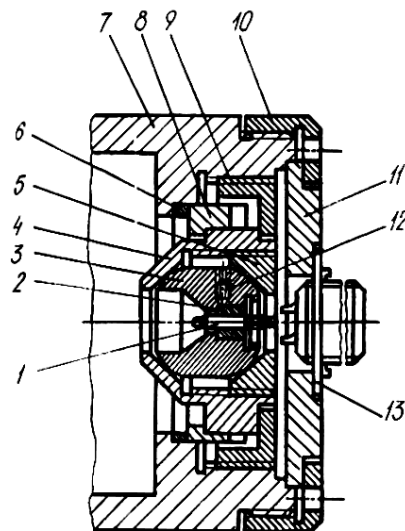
Пристрій для кріплення світлодіода з його центруванням, фокусуванням та регулюванням напрямлення випромінювання: 1 — світлодіод; 2 — оправа; 3 — втулка шарова; 4 — оправа; 5, 9 — кільця різьбові; 6 — кільце підрізне; 7 — корпус; 8 — кільце ексцентричне; 10 — гайка; 11 — втулка; 12 — гвинт; 13 — живлення
